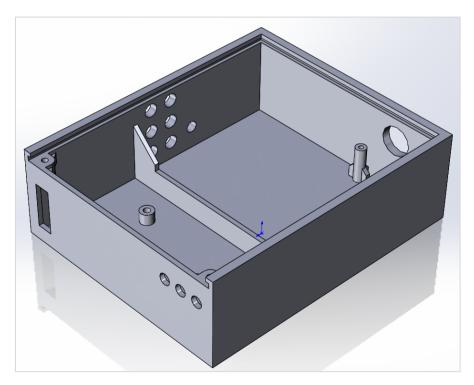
Общий вид нового корпуса, часть 2
